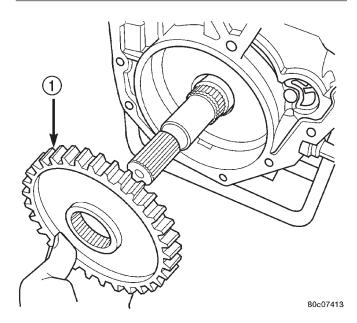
Desmontaje del engranaje de calce de estacionamiento
